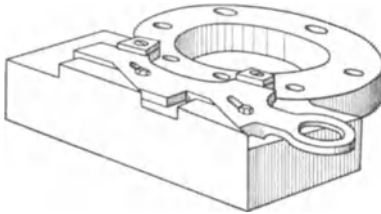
Bohrflansch mit Ausrichteanschlügen.
